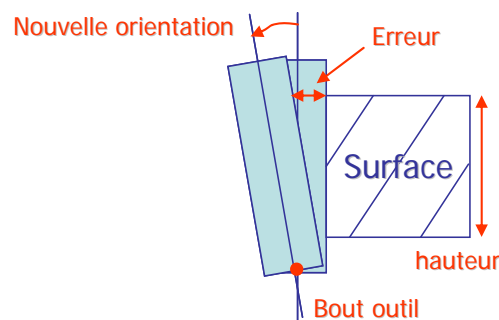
Erreur sur la surface dans le cas de l'usinage en flanc
